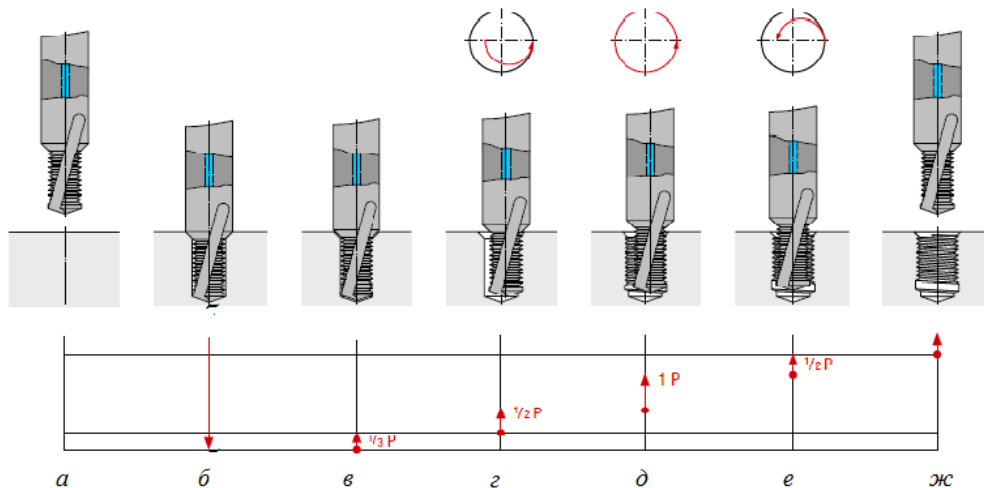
Кинематическая схема процесса обработки сверлом-резьбофрезой [5, 7]
